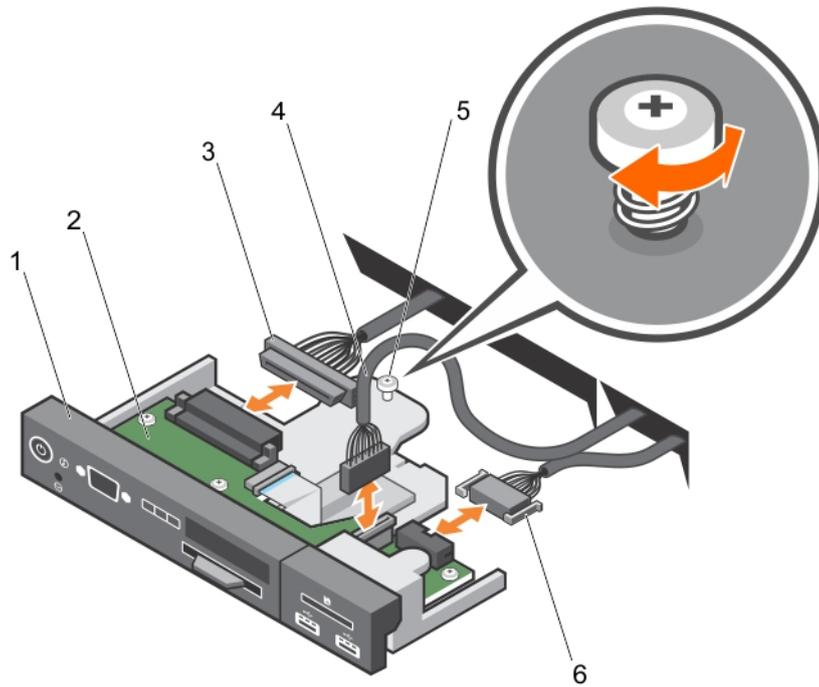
Entfernen und Einsetzen des Bedienfeldes – System mit 3,5-Zoll-Festplatten – PowerEdge R730
